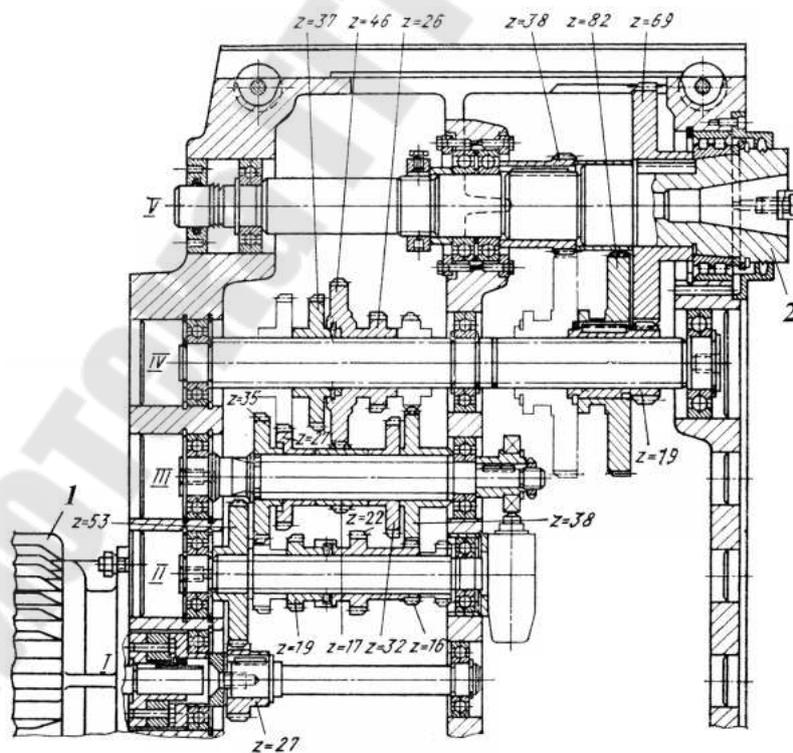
Коробка передач горизонтально-фрезерного станка:
